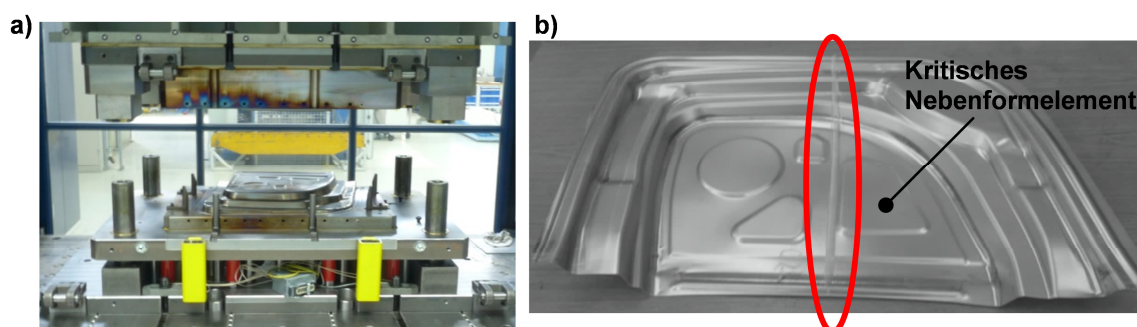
SMiLE-Ziehwerkzeug und gezogene Innentür mit Markierung des betrachteten Schweißnahtbereichs
